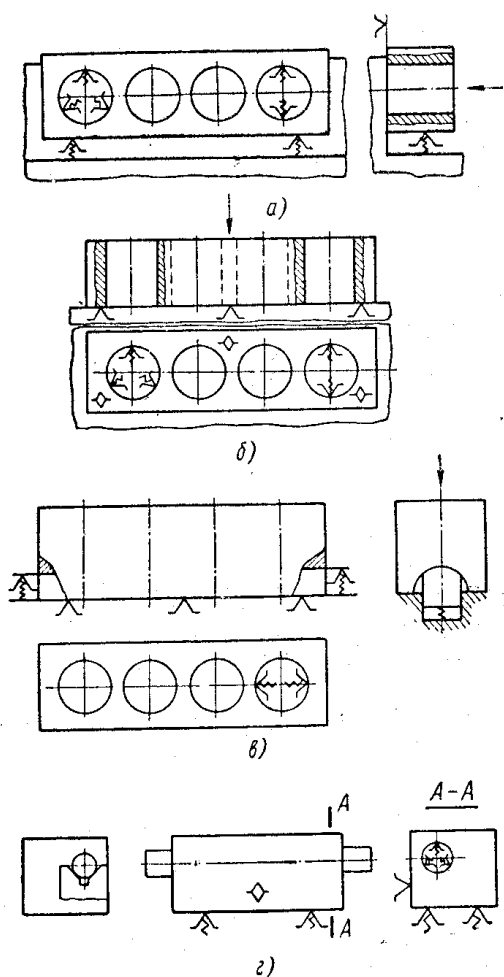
Схема базування корпусних деталей по необроблюваних отворах і площині
